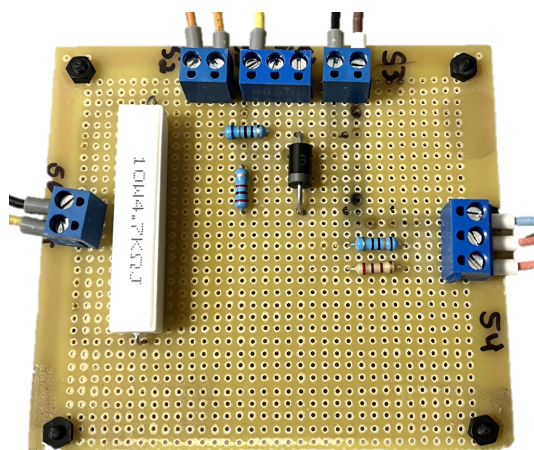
Placa com os componentes soldados. Fonte: Elaboração Própria.
